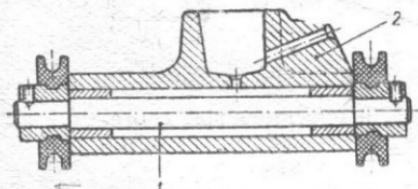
Промежуточный вал наматывателя в разрезе: 1—промежуточный вал; 2—подшипник
